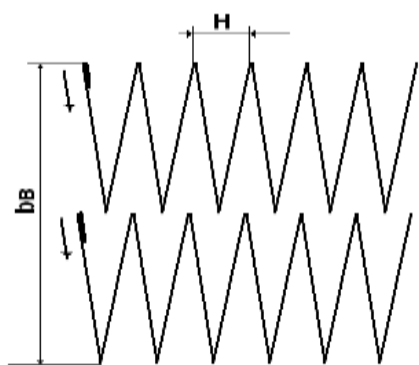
Способ ширококослойной наплавки двумя электродными проволоками
